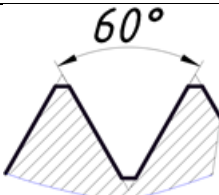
Образец выполнения резьба с нестандартным профилем
